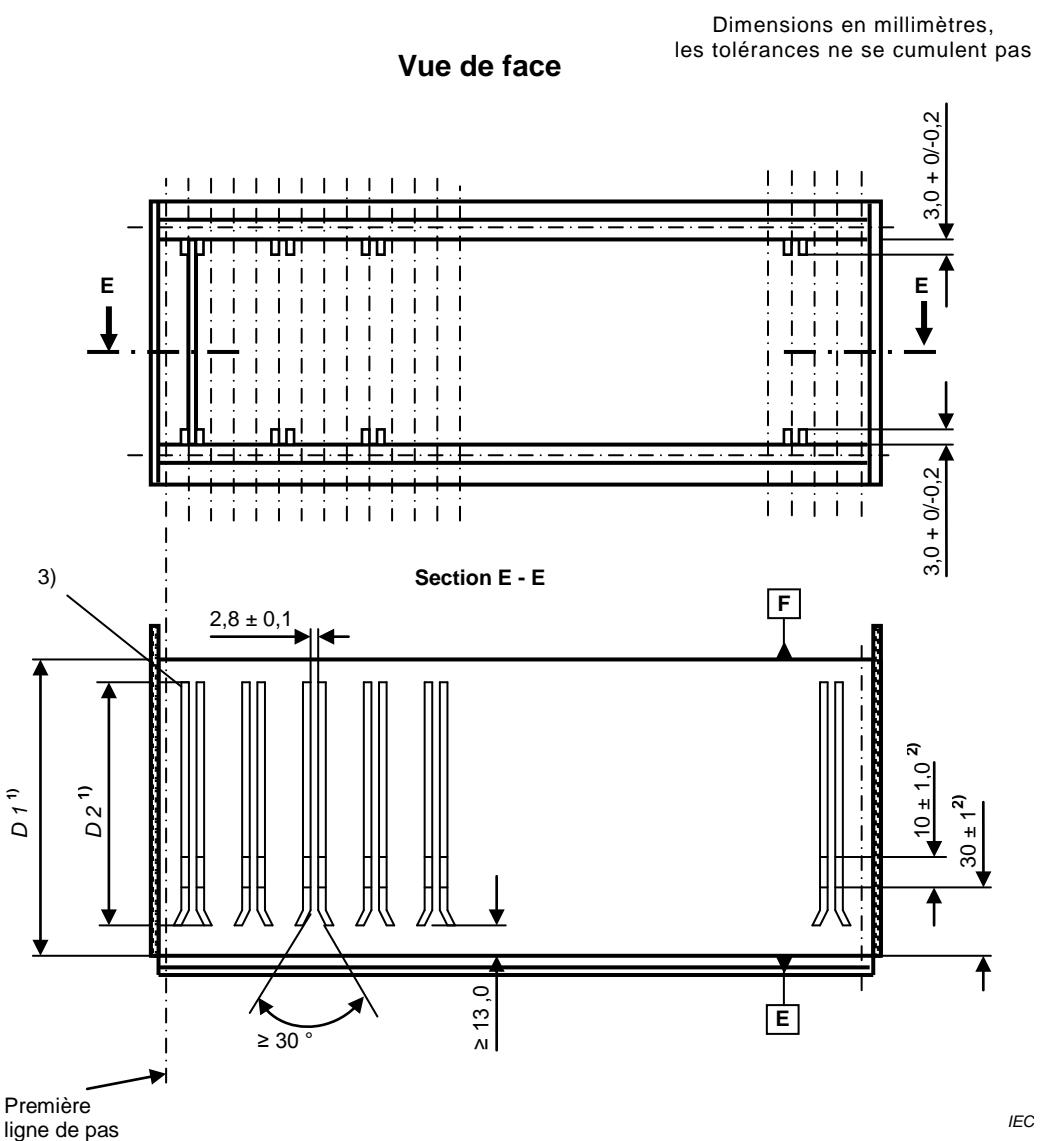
Dimensions de montage arrière d'un bac de type RB
